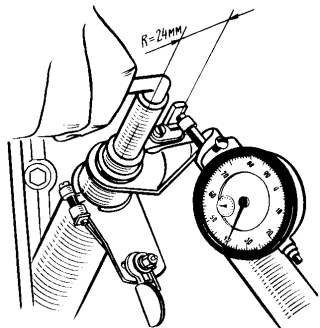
Проверка бокового зазора в зацеплении шестерен привода масляного насоса и прерывателя-распределителя
